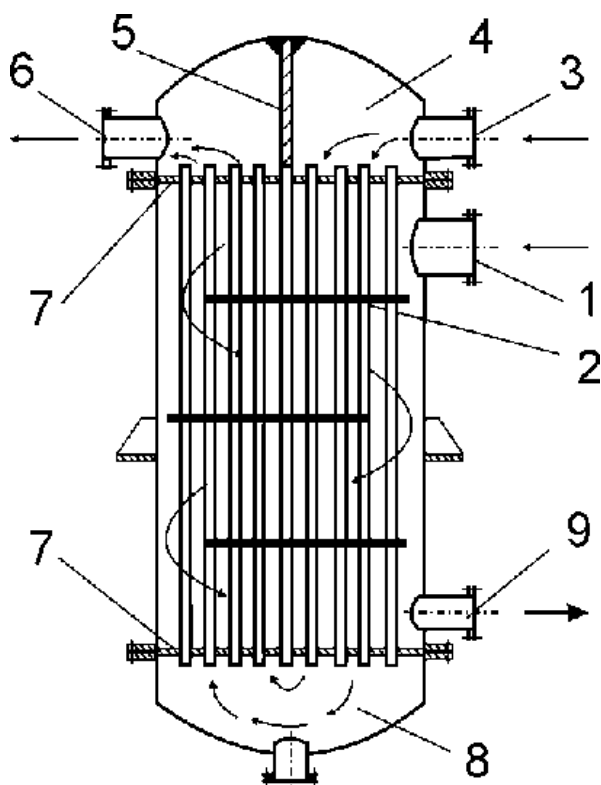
Двухходовой аппарат жесткой конструкции: 1 – патрубок для входа пара; 2 – направляющие перегородки; 3, 6 – патрубки для входа и выхода черного щелока; 4, 8 – верхняя и нижняя растворные камеры; 5 – разделительная перегородка; 7 – трубные доски
